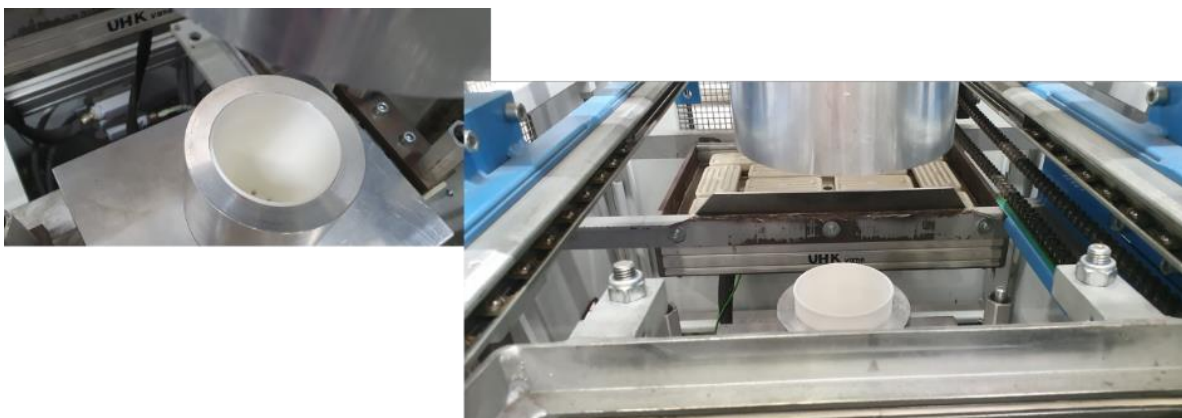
Thermoforming-Werkzeug mit dem Einsatz für den Systemlayer (links); Systemlayer überragt Einsatz (rechts)
